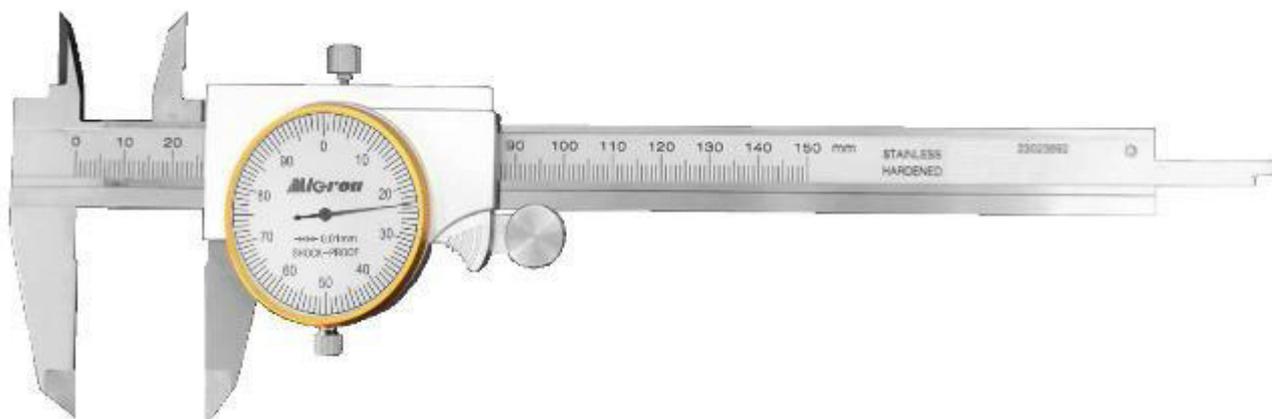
Общий вид штангенциркулей типа ШЦК-I с круговой шкалой в миллиметрах и расположением стопорного винта в средней части рамки
